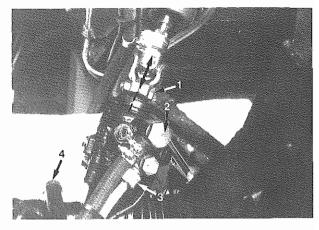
1 - Vite fissaggio fascetta inferiore Lower clamp screws
